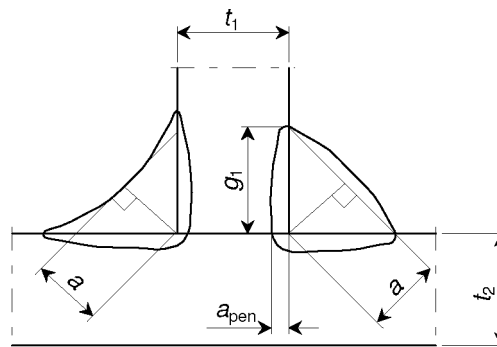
Розрахункова товщина зварного шва a ; проплавлення кореня шва a_{pen}
